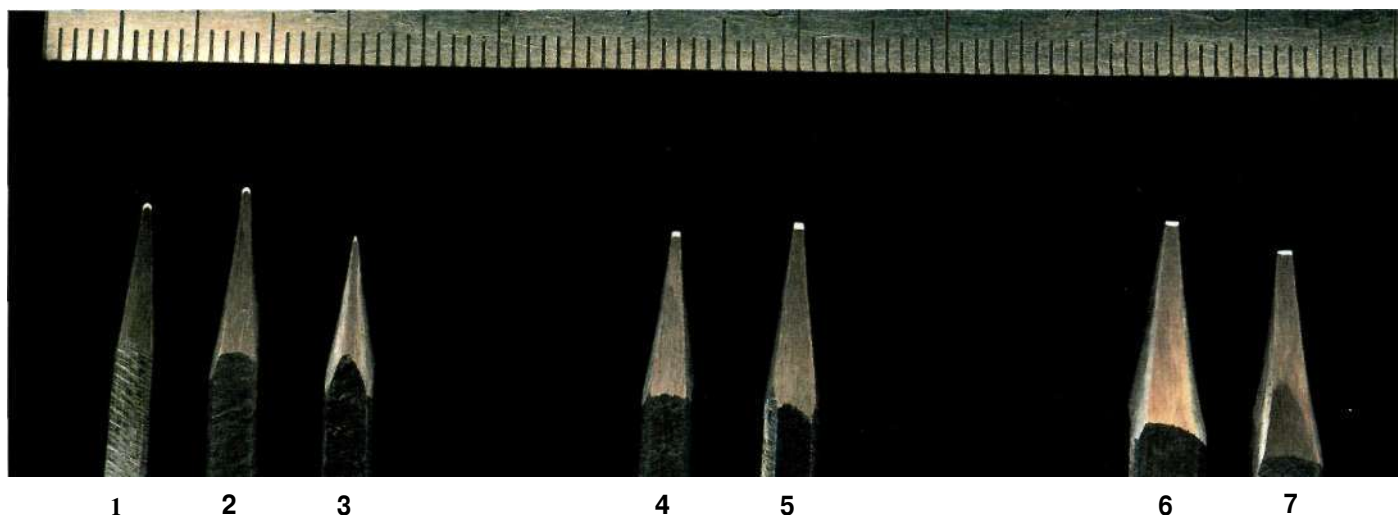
а. Зубильца и керн: рабочие поверхности (увеличение). Вид спереди
